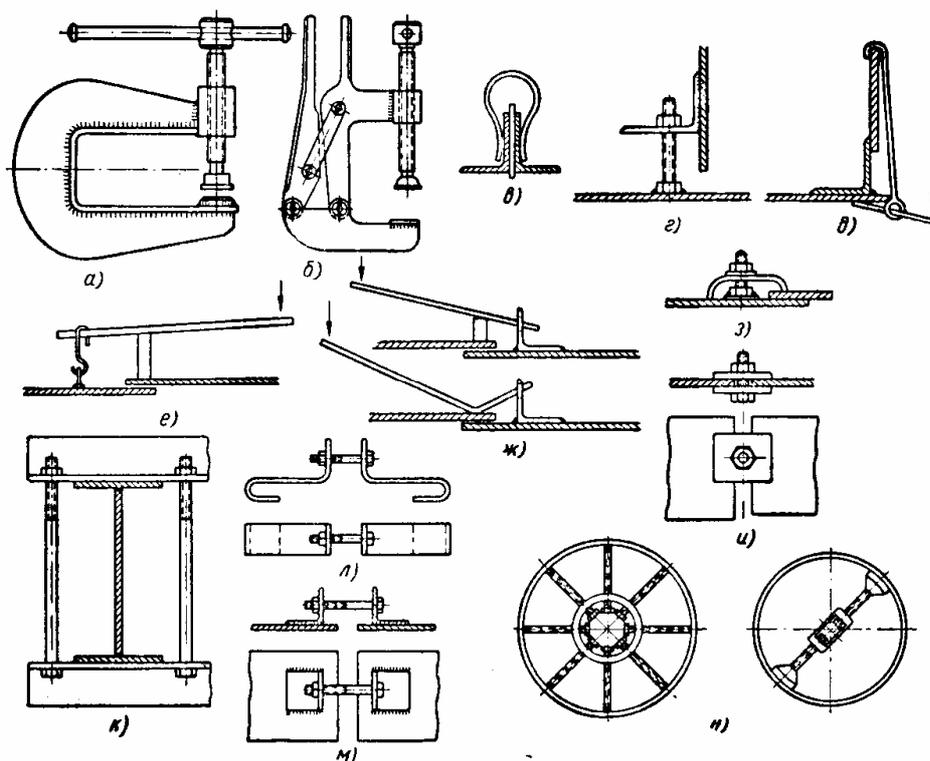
Приспособления для сборки сварных конструкций:
